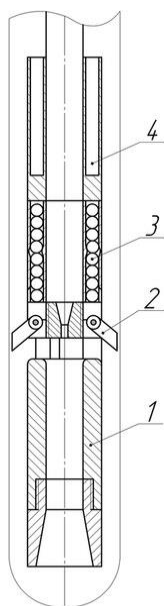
Схема компоновки низа буровой колонны с улавливающе-подпитывающим устройством:
